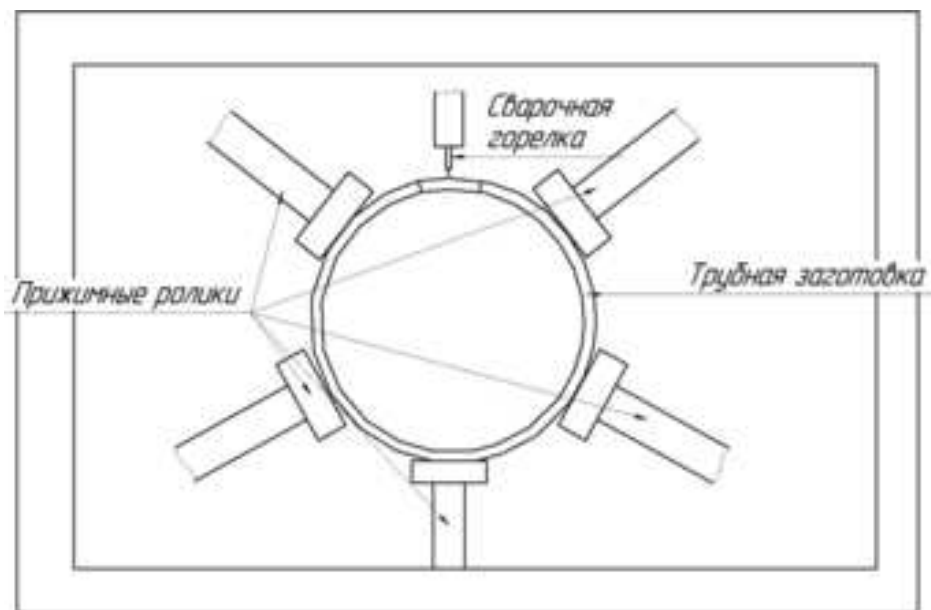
Сборочно-сварочный стан
